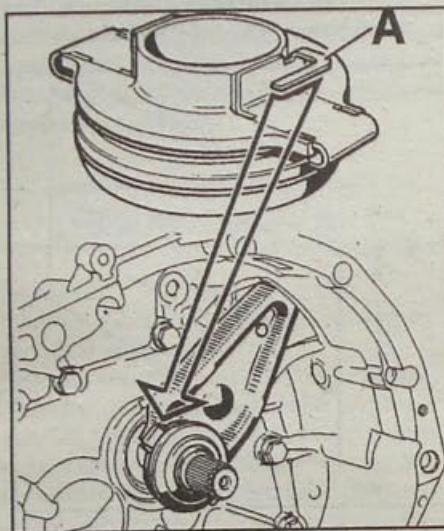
Установка подшипника выключения сцепления на направляющую втулку:
